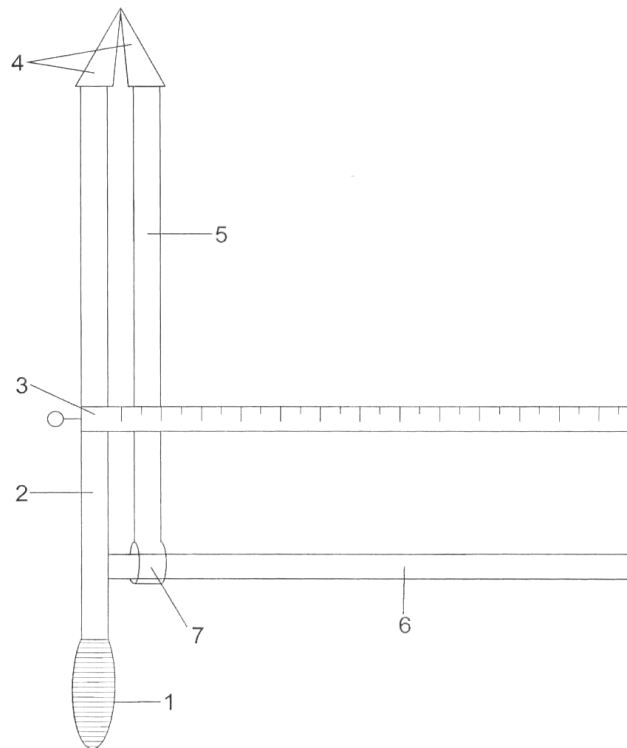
Схематичне креслення нової конструкції вимірювального циркулю.
